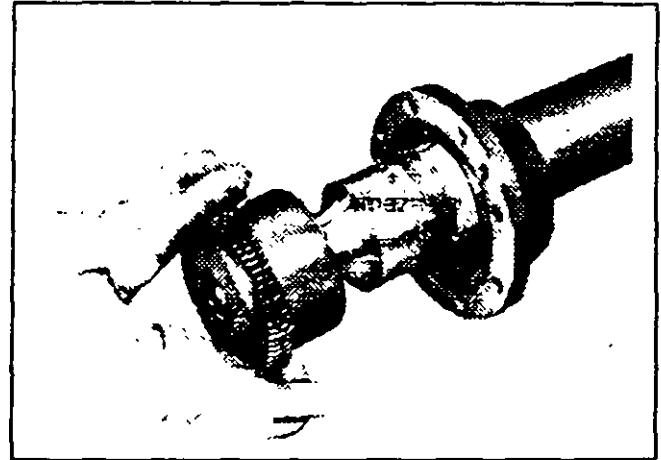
APLICANDO LA MAZA DE ACOPLAMIENTO CALENTADA A LA FLECHA IMPULSORA DEL COMPRESOR. E-25402-S
